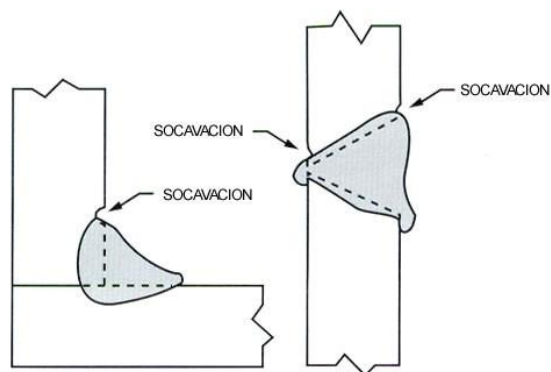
Socavación en raíz y cara de soldadura.
